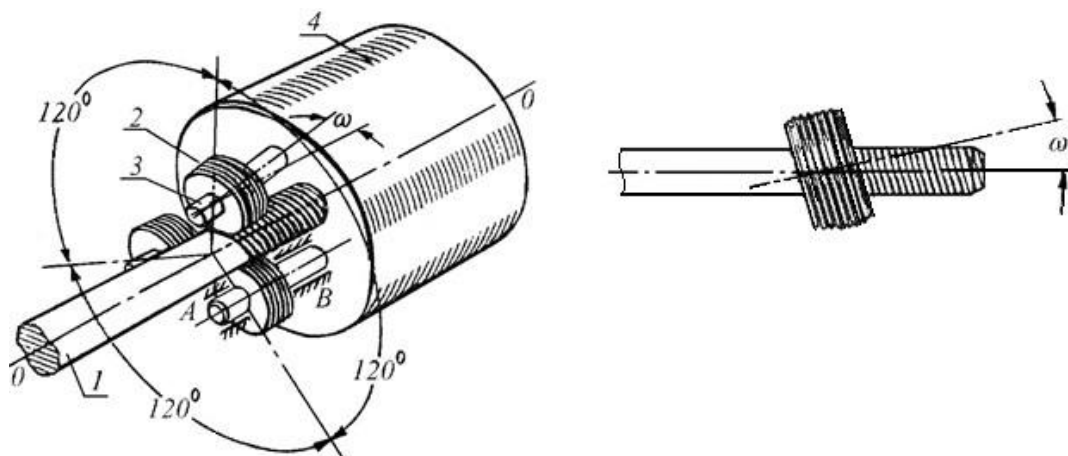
Схема різенакатувальної головки, яка працює з осьовою подачею
